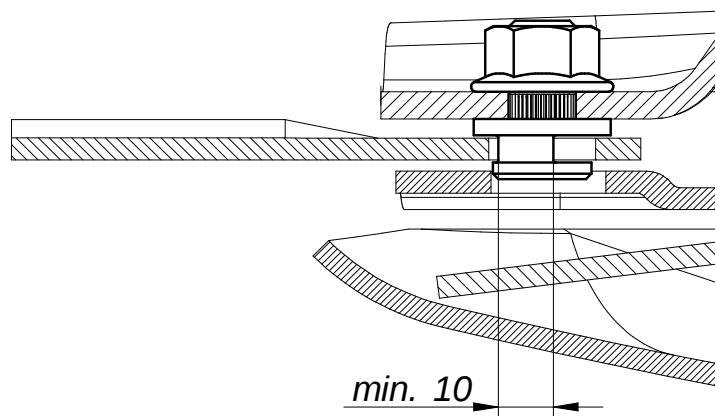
Допускаемое изношение стержня держателя ножей в диске
